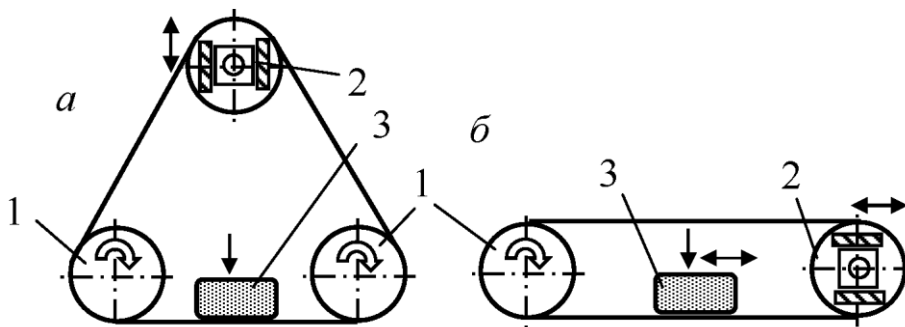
Механізми головного руху стрічкових шліфувальних верстатів: а - трьохбарабанний; б - двобарабанний
